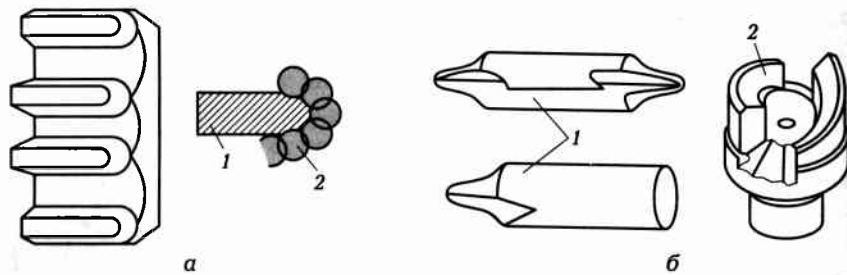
Схема зубозакругления (а) и конструкции фрез для округления зубьев (б)
